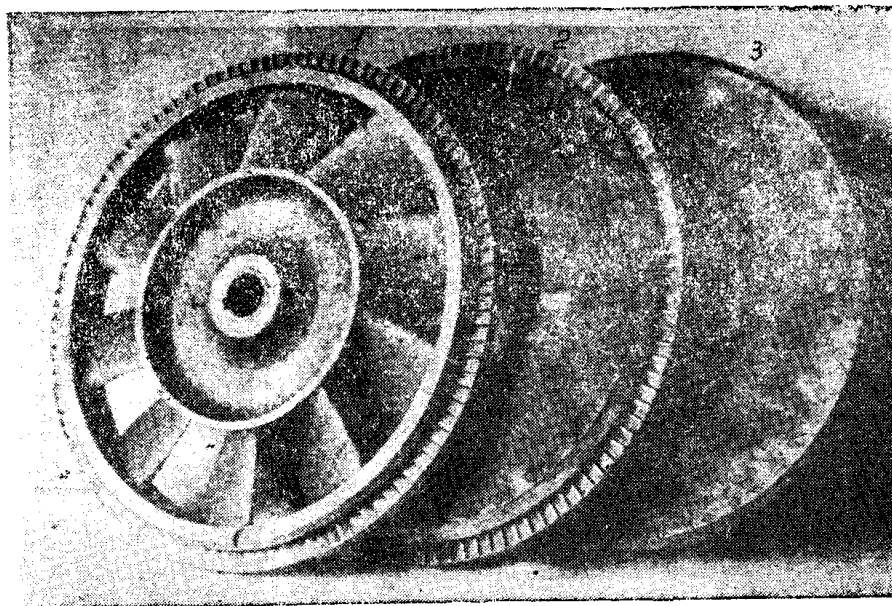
Рабочие колеса пневматического вентилятерного агрегата: 1—в нормальном исполнении; 2—с заглушенными лопатками вентилятора; 3—с заглушенными лопатками вентилятора и без лопаток турбодвигателя.
